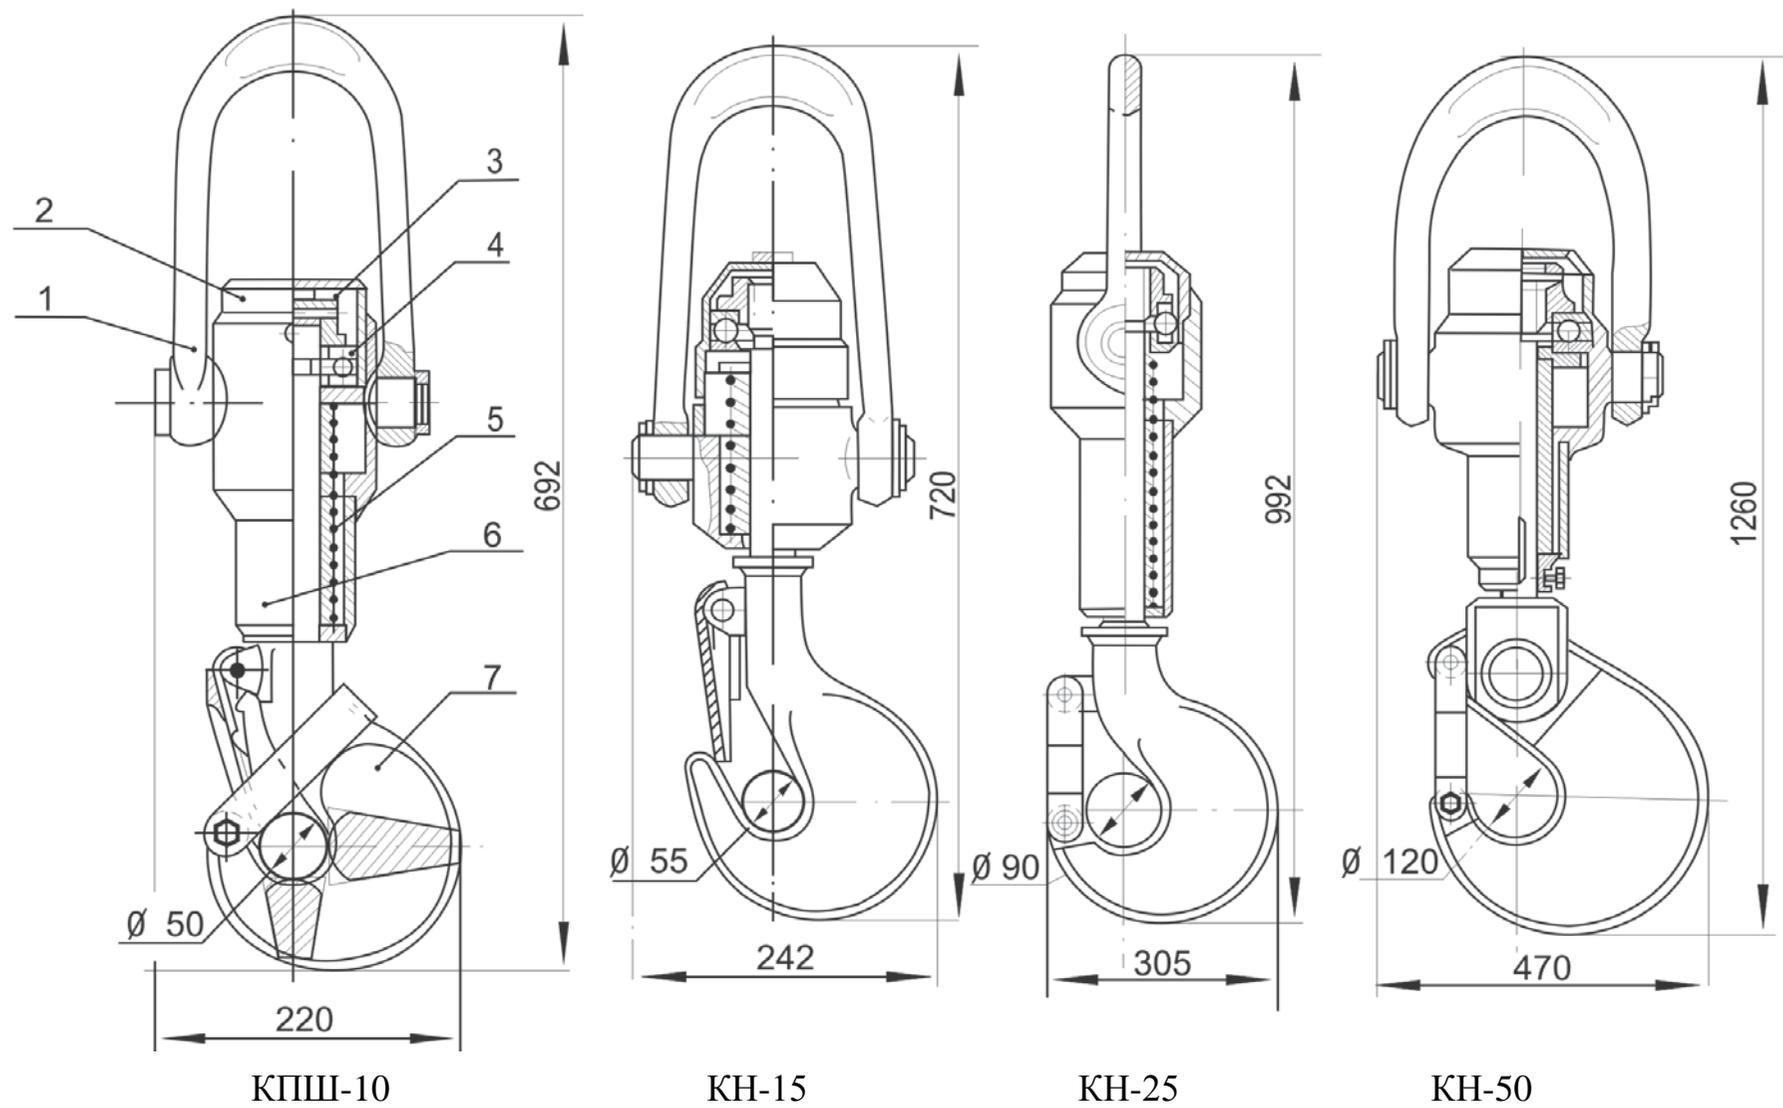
Крюки: 1-кожух; 2-штроп; 3-гайка; 4-упорный подшипник; 5-пружина; 6-корпус крюка; 7-рог
